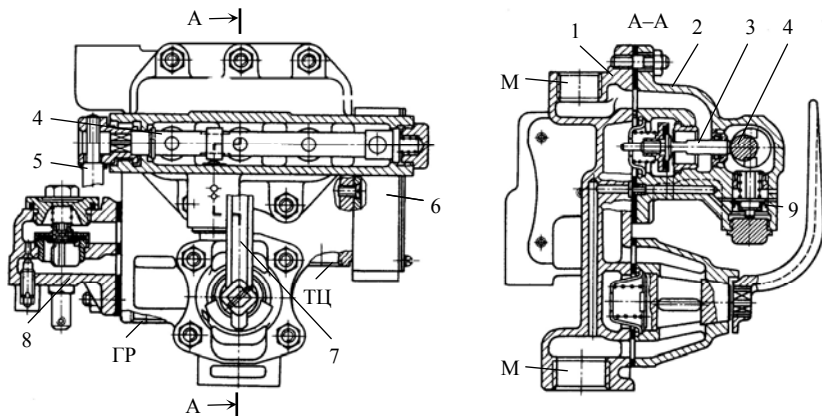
Устройство № 367М блокировки тормоза локомотива
